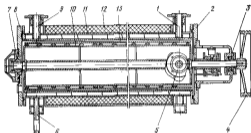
Теплообменный корпус аппарата А9-КБД с очищаемой поверхностью:
